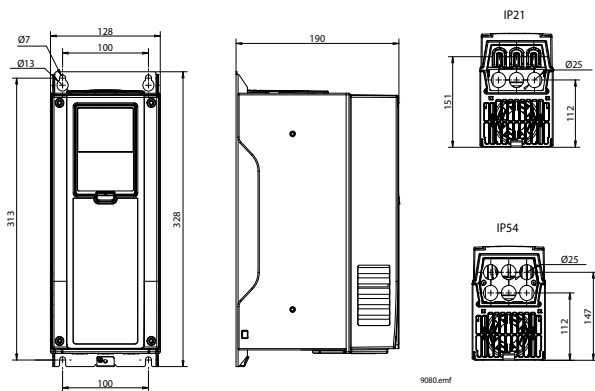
Dimensões do inversor de CA Praxi, MR4, montagem na parede
